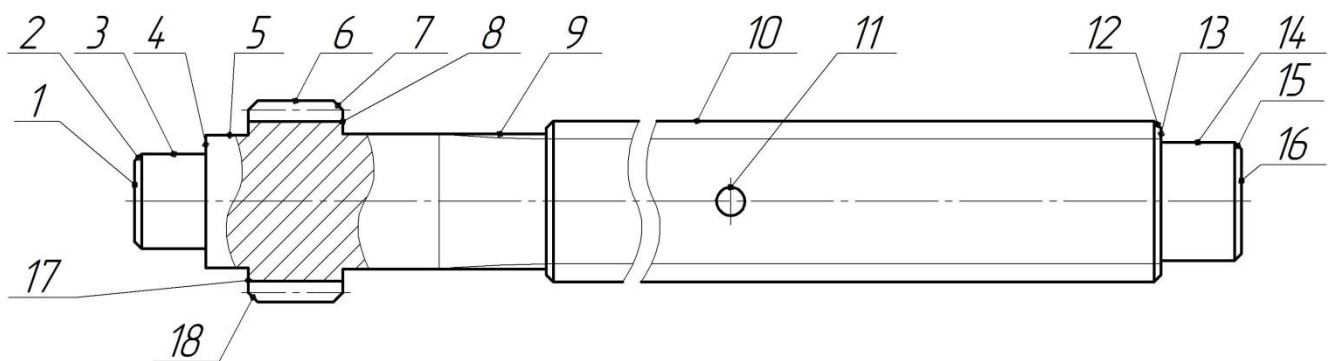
Ескіз деталі з номерами поверхонь
